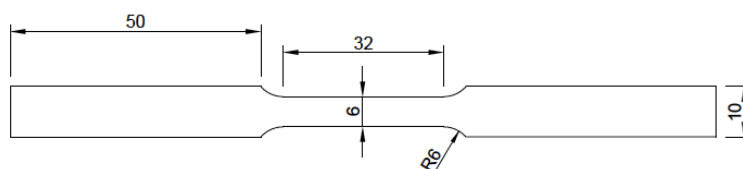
Dimensões do corpo de prova. [Adaptado de ASTM E8 / E8M -15a].
